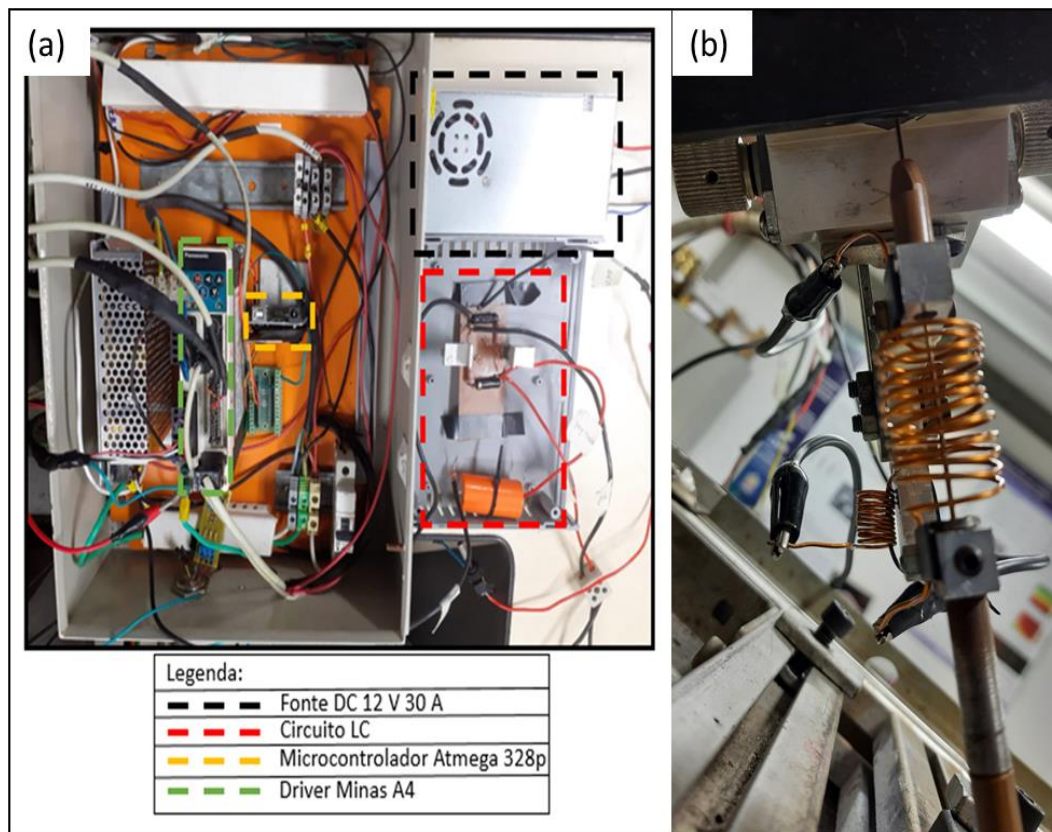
Circuito eletro/eletrônico (a) e bobina de pré-aquecimento (b)
